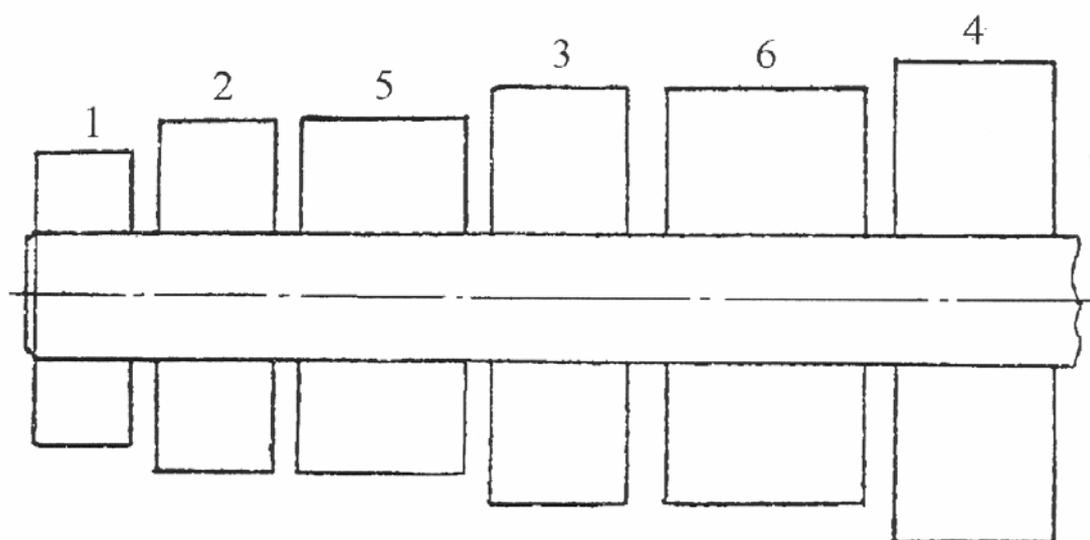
Примерное соотношение габаритных размеров подшипников качения одного и того же внутреннего диаметра, но разных серий:
